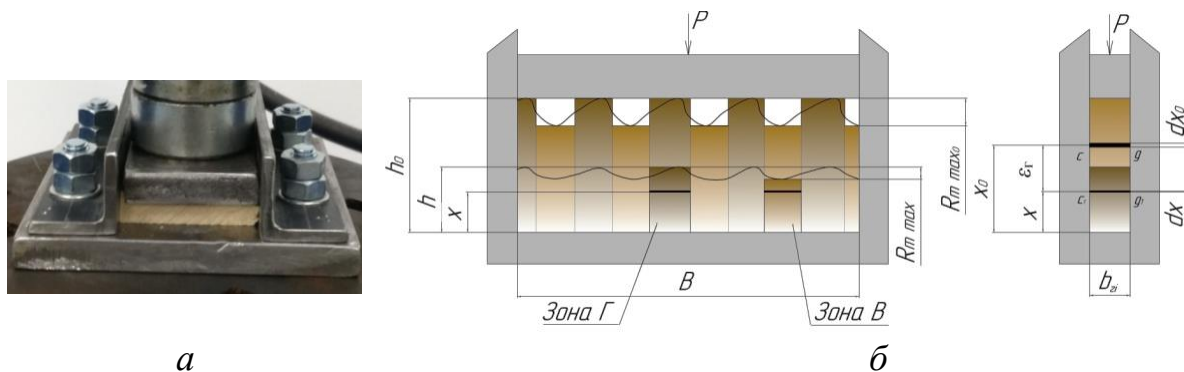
Прессование заготовки, подвергнутой обжигу и брашированию:
